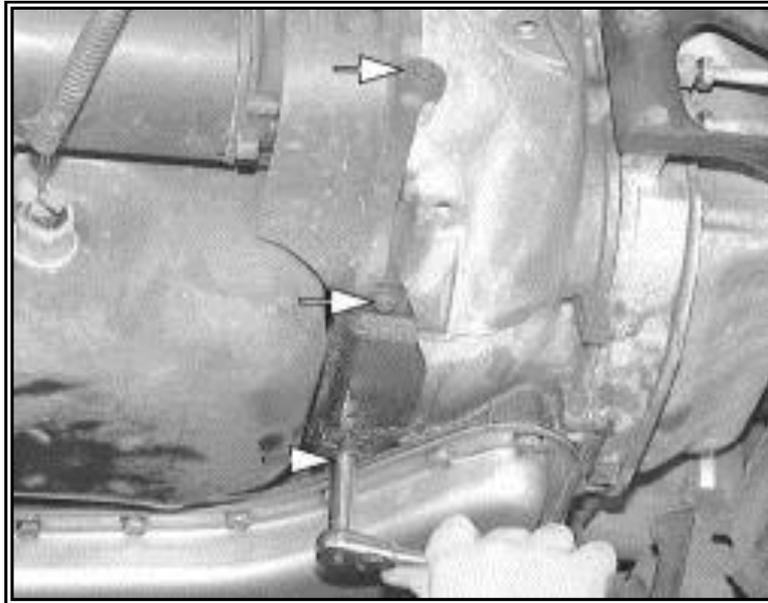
Desmontaje cubierta campana. (AutoZone, 2018)
